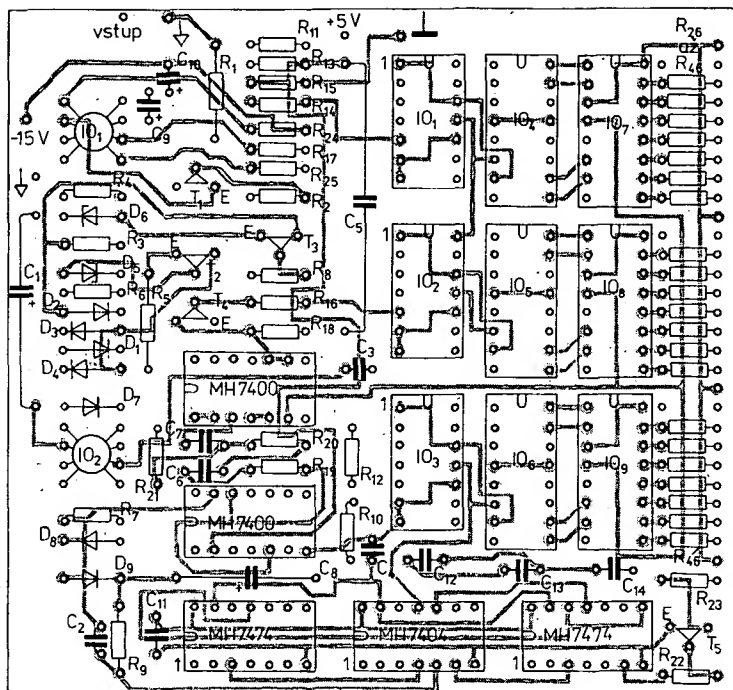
Obrazec plošných spojů P223 panelového měřidla, strana spojů – pohled ze strany spojů
